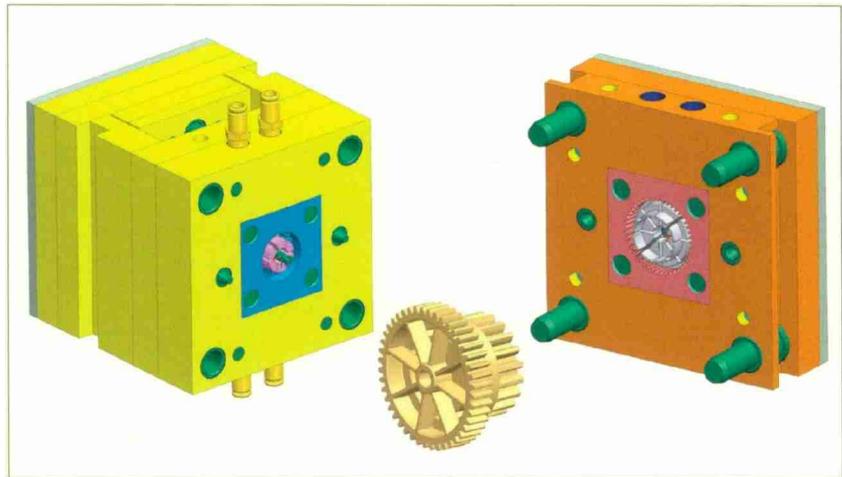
Moule de test et pièce injectée de référence. (images: iRAP)
